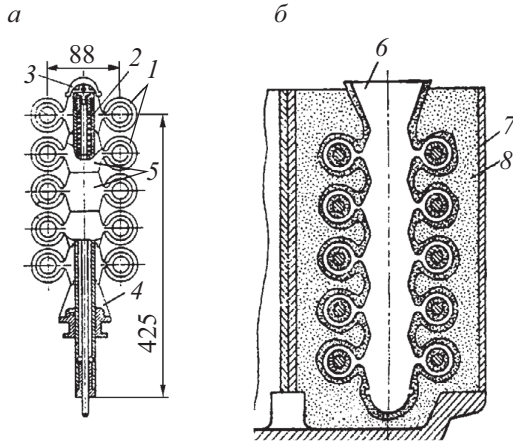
Модельный блок (а) и оболочковая неразъемная литейная форма (б) для получения заготовок:
